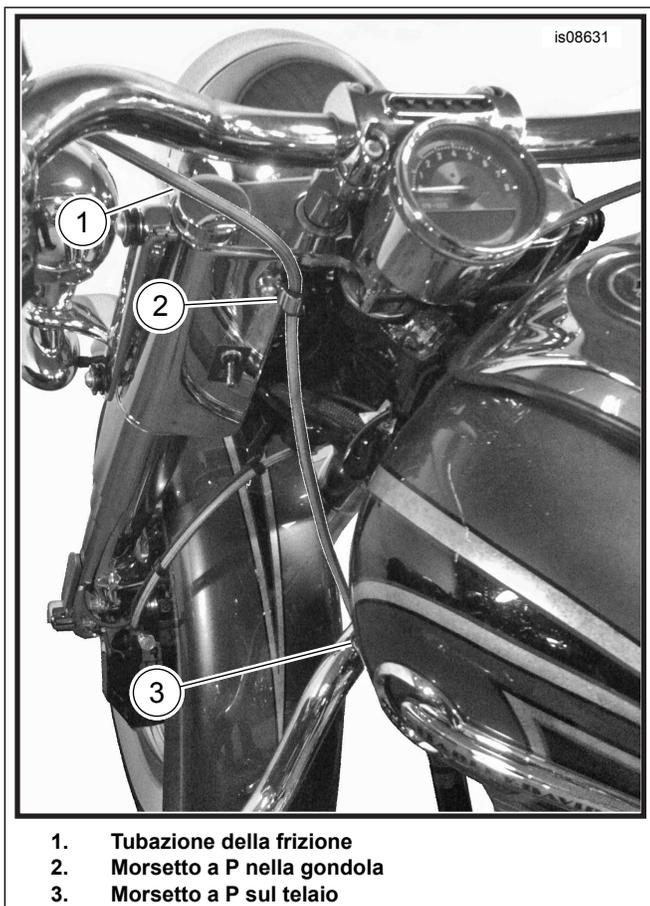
Disposizione superiore della tubazione idraulica della frizione (modelli Softail)
